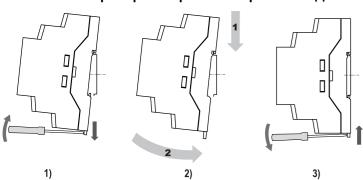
Монтаж прибора с креплением на DIN-рейку
